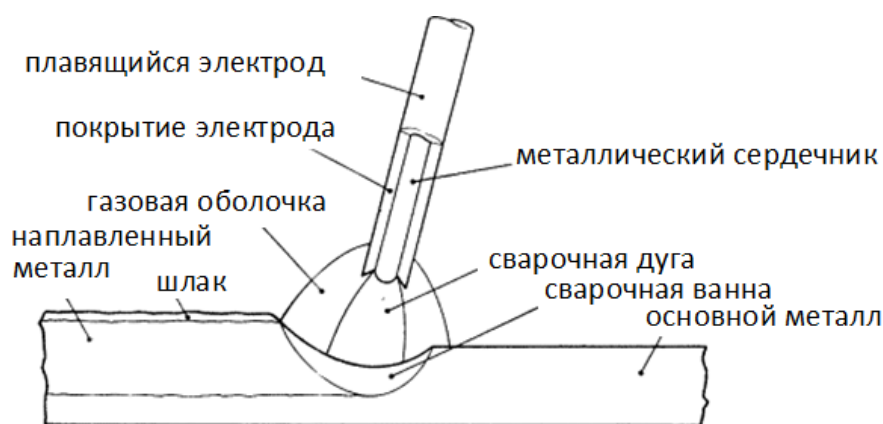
Схема выполнения ручной дуговой сварки
